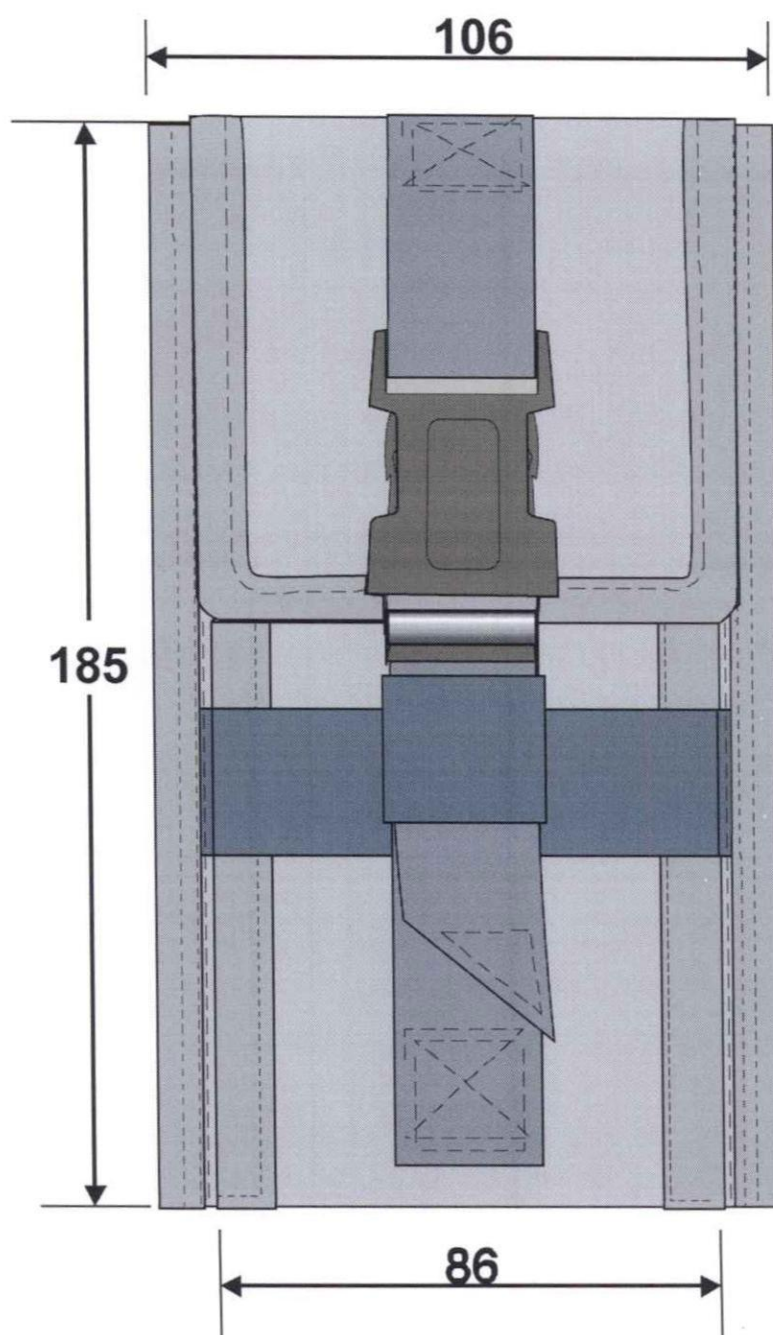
Vista frontal do estojo (medidas em milímetros)
